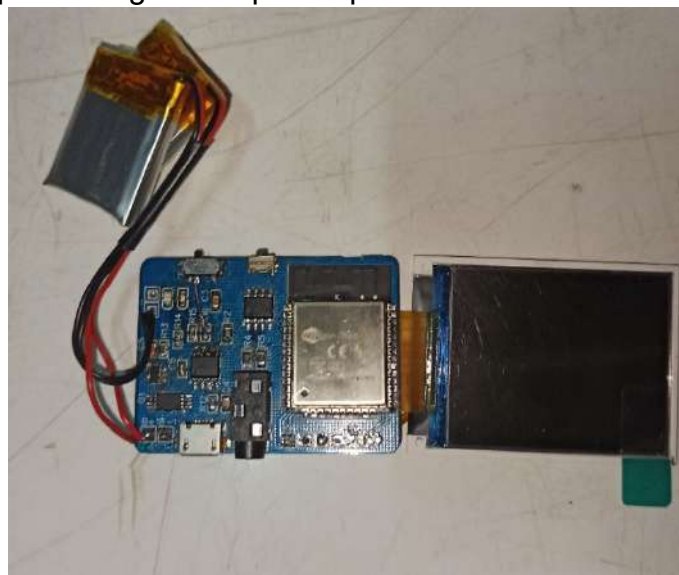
Sampel Beberapa Hasil Cetak PCB
